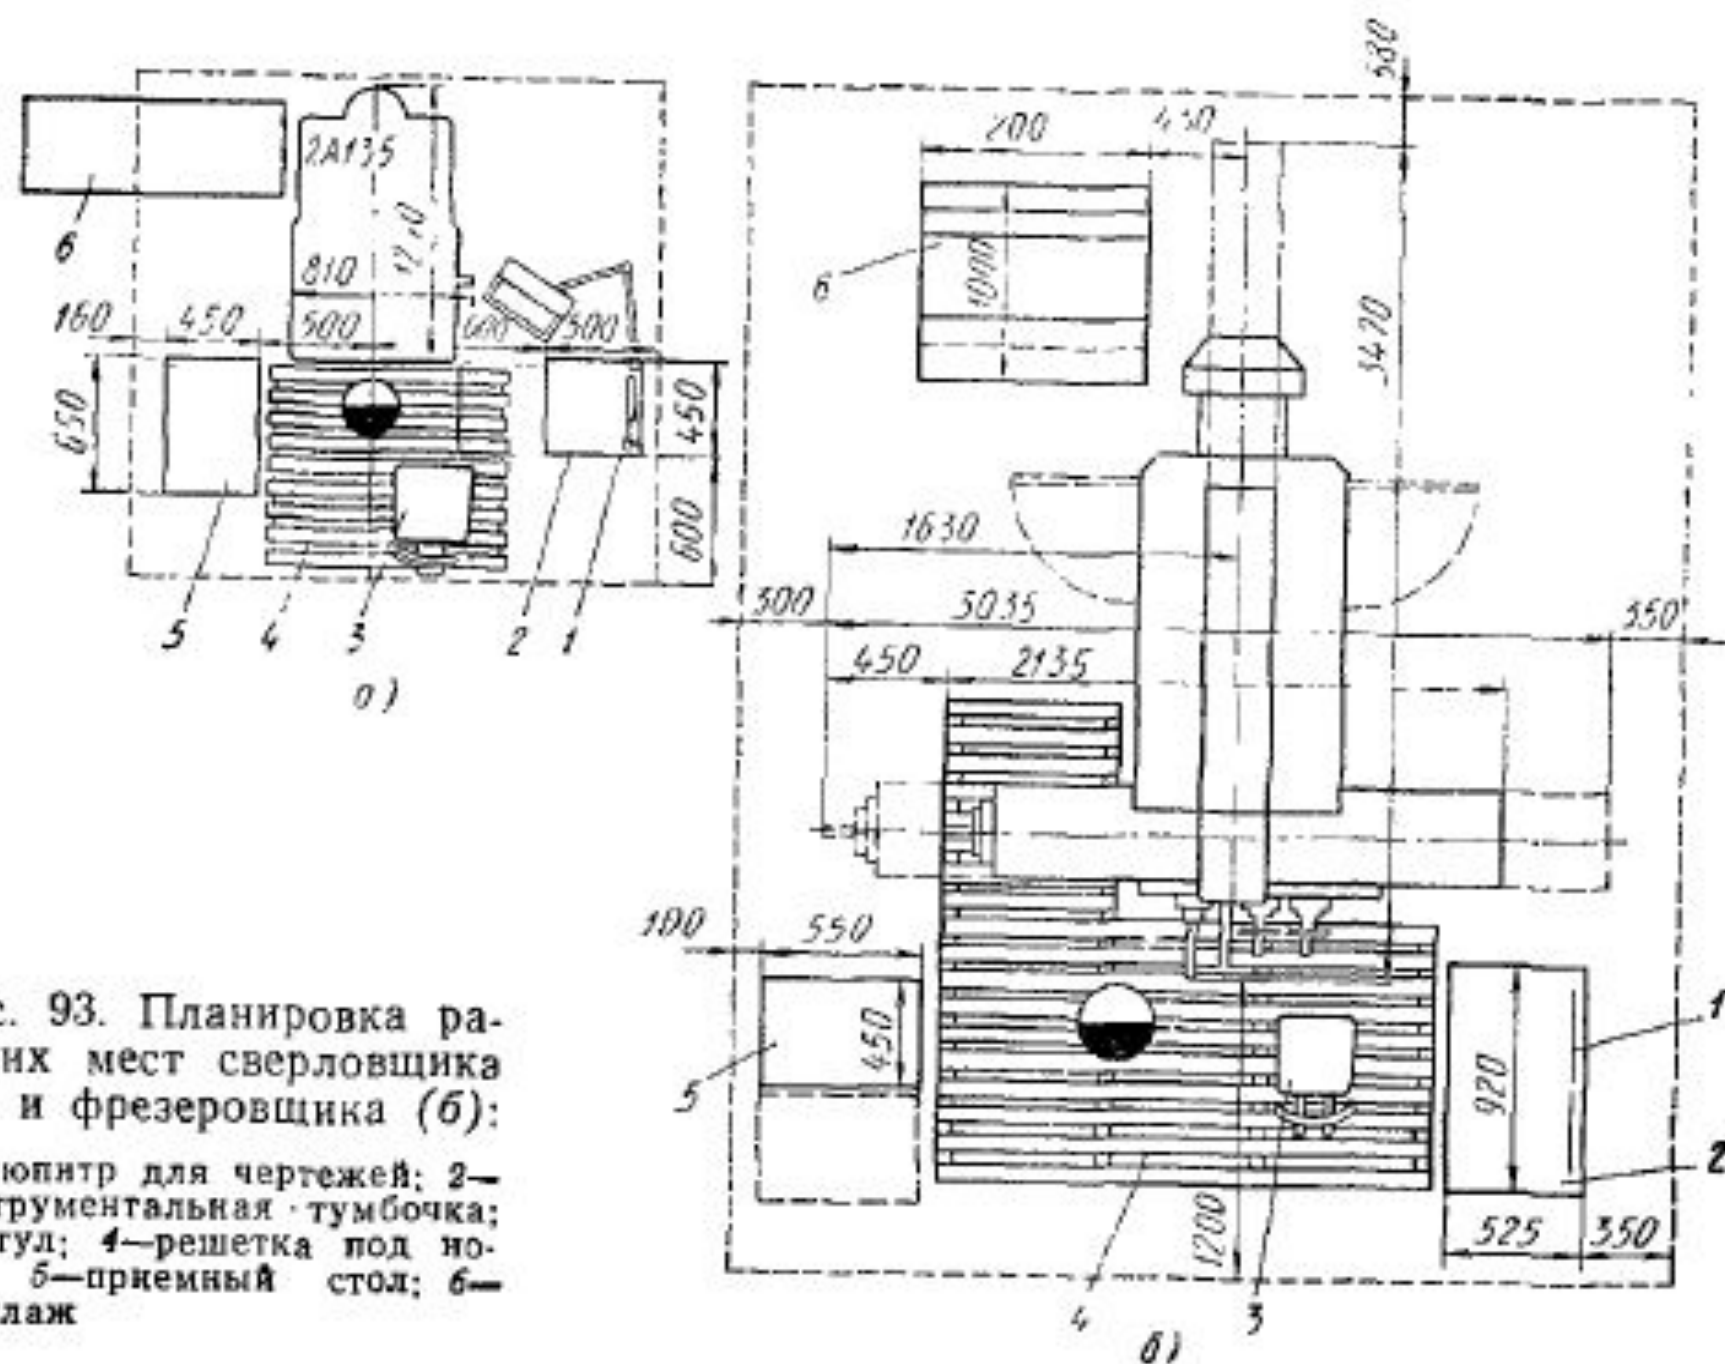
Планировка рабочих мест сверловщика (а) и фрезеровщика (б):
